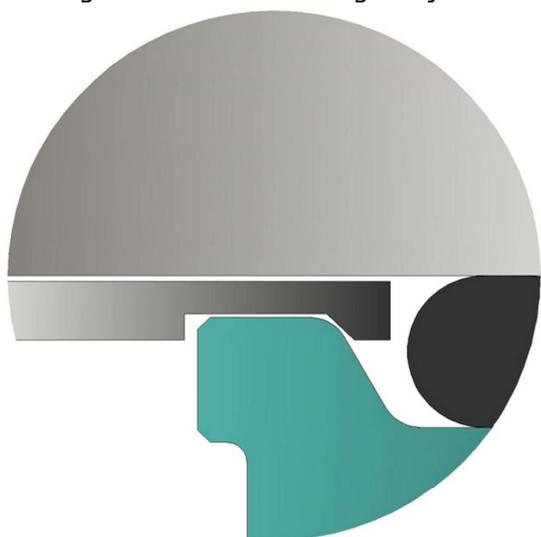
Enlever le siège du joint, extrémité en forme de crochet
